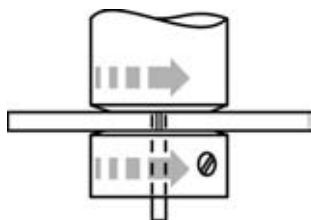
Схема сварки инструментом в виде катушки (Bobbin Tool)
